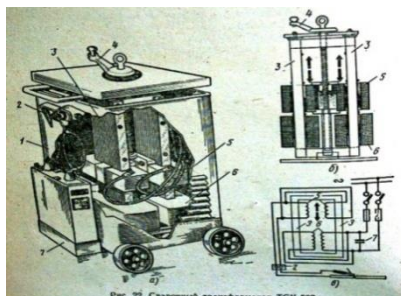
Сварочный трансформатор ТСК-500.
